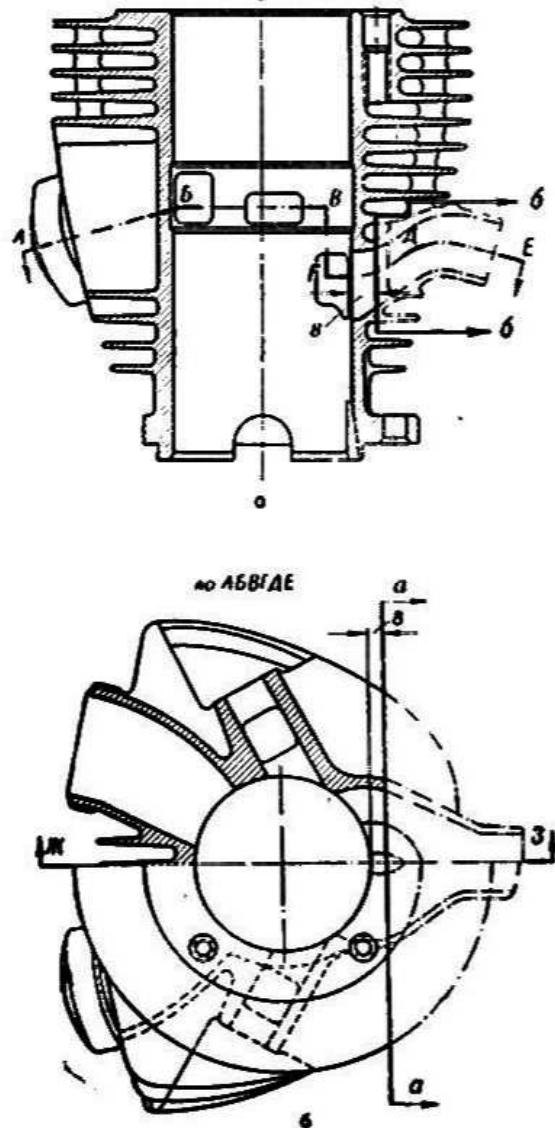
Подрезка патрубка цилиндра двигателя ИЖ-350 или ИЖ-49:
